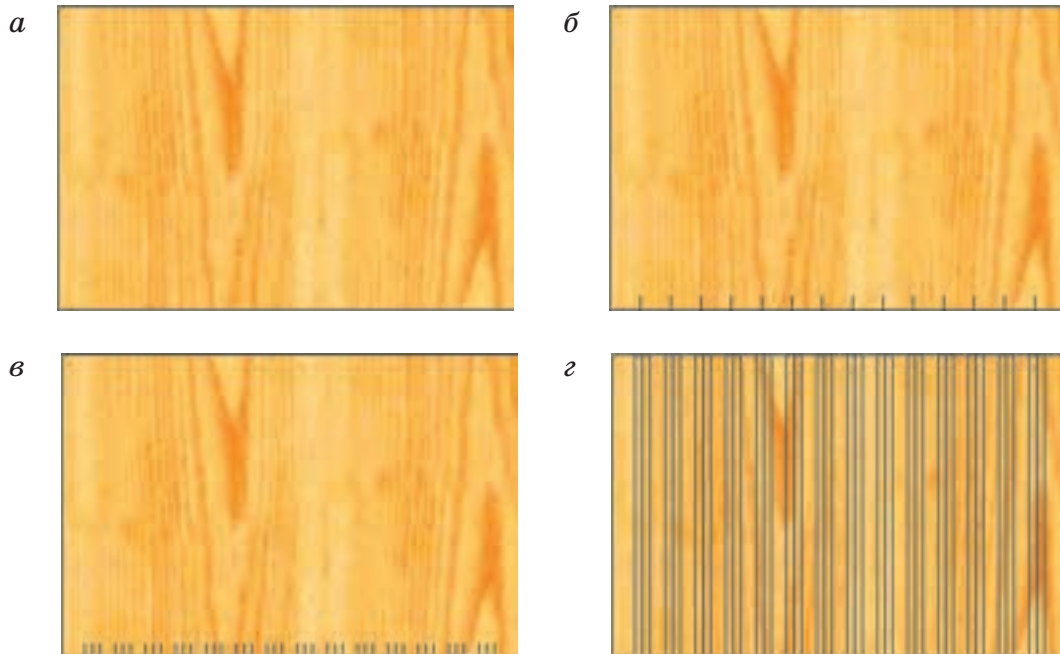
Последовательность разметки заготовки для выполнения двугранных выемок
